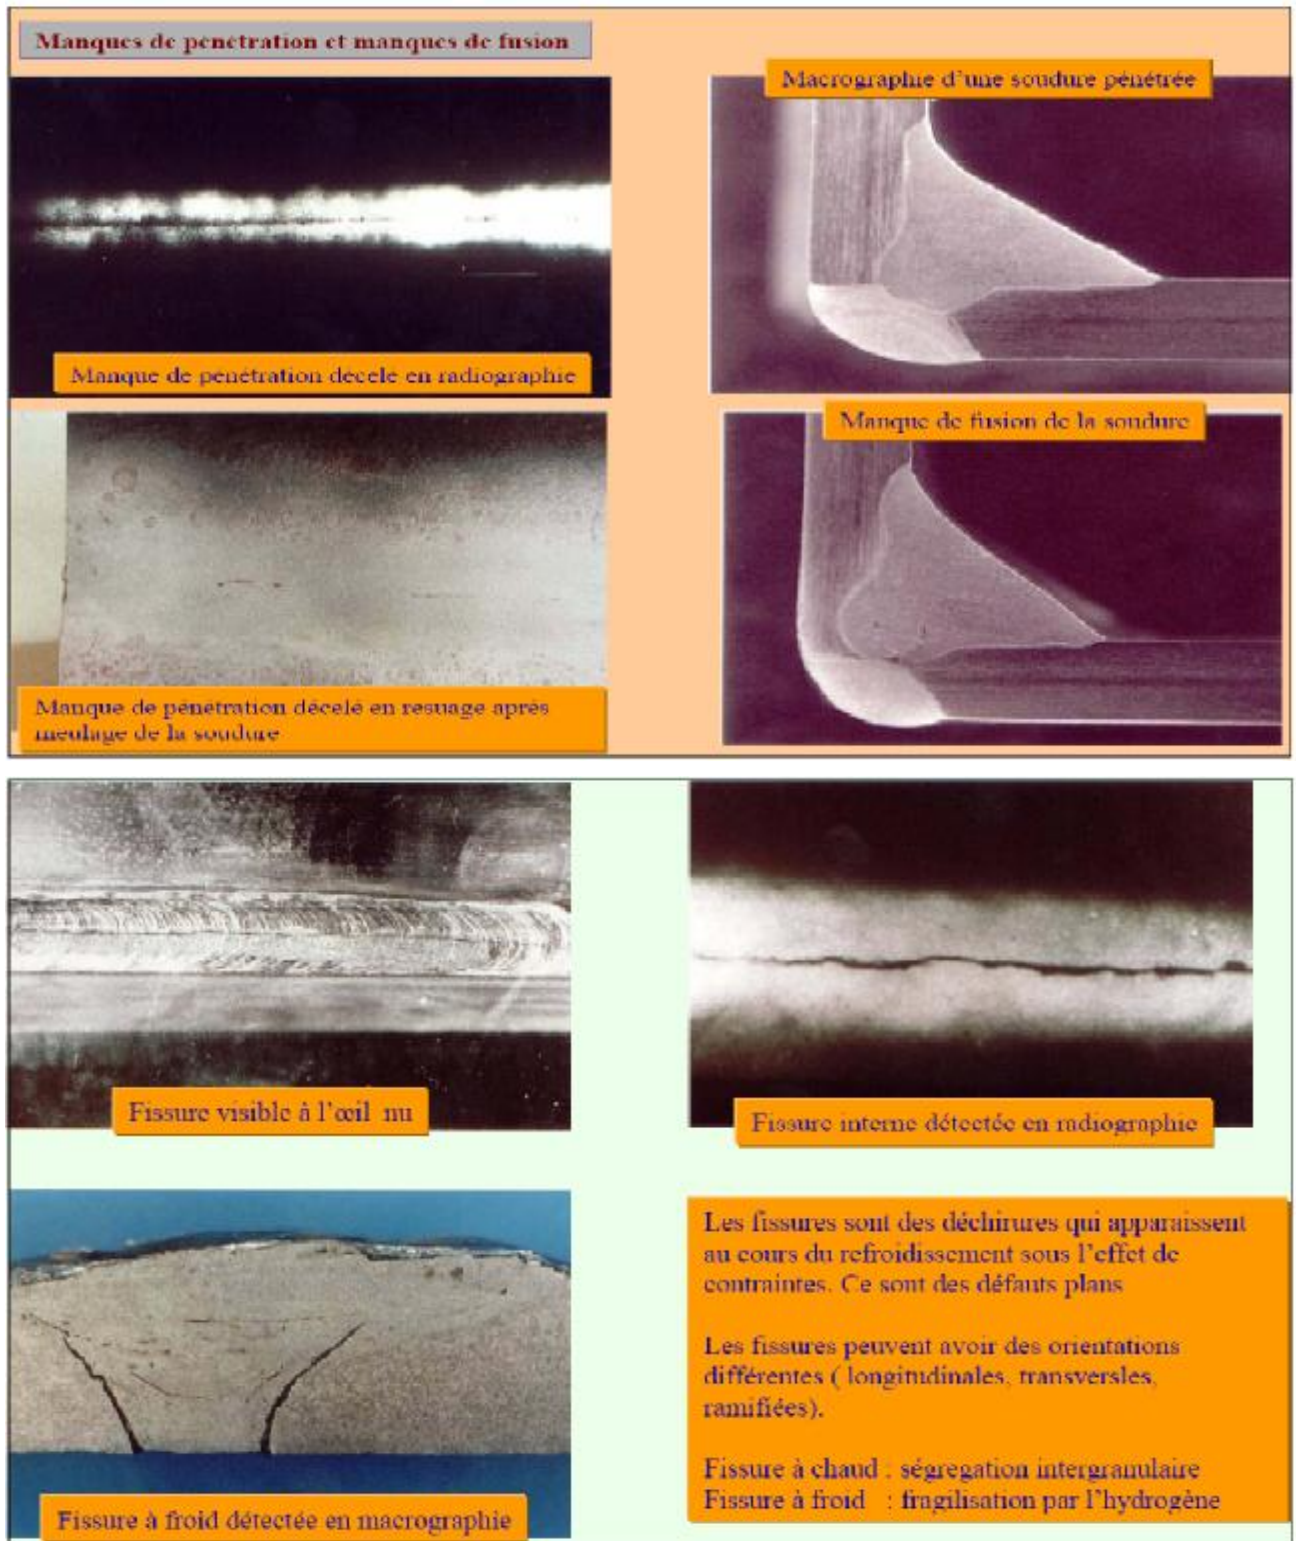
Défauts interne de soudure pouvant être détectés par radiographie, resuage, visuellement et macrographie
